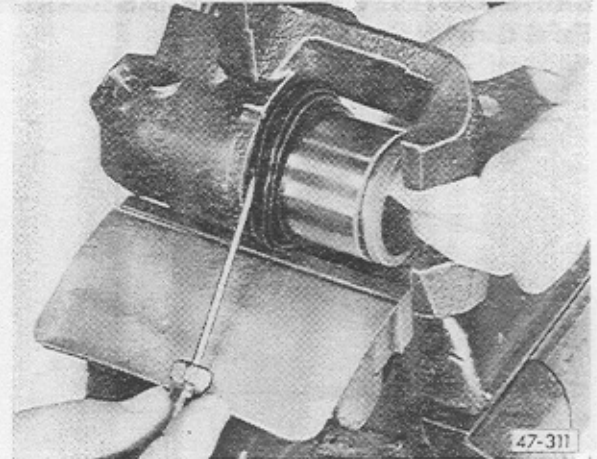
Innere Dichtlippe der Schutzkappe mit einem Schraubenzieher in die Nut des Zylinders einsetzen
